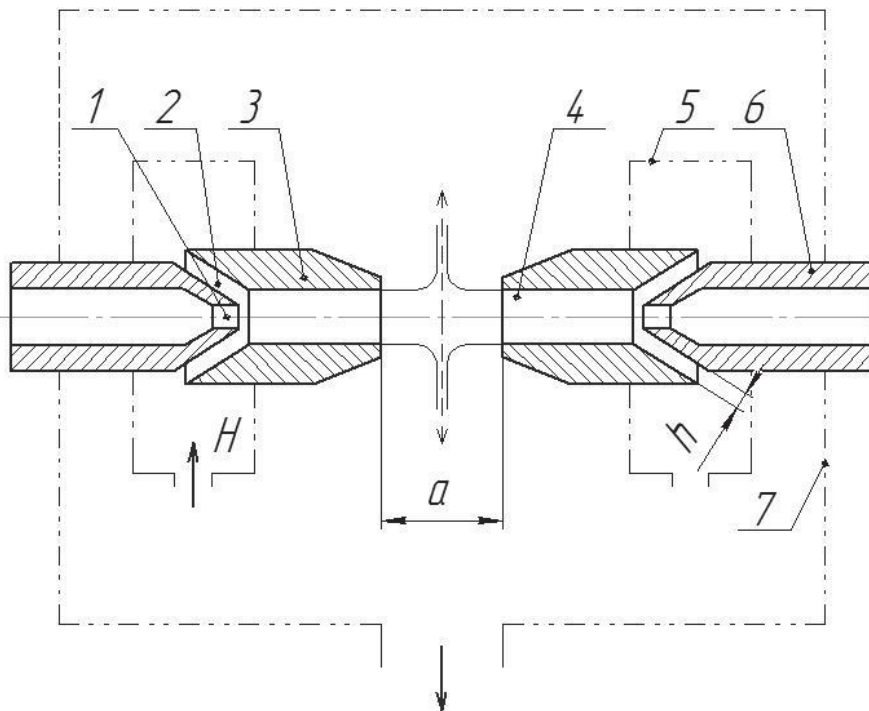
Схема протитечійно-струминного змішувача: 1 – робоче сопло; 2 – камера ежекції; 3 – камера змішування; 4 – сопло камери змішування; 5 – камера подачі концентрату; 6 – робочий патрубок; 7 – камера збору рідини; a – відстань між соплами; H – напір подачі концентрату; h – кільцевий зазор камери ежекції.
